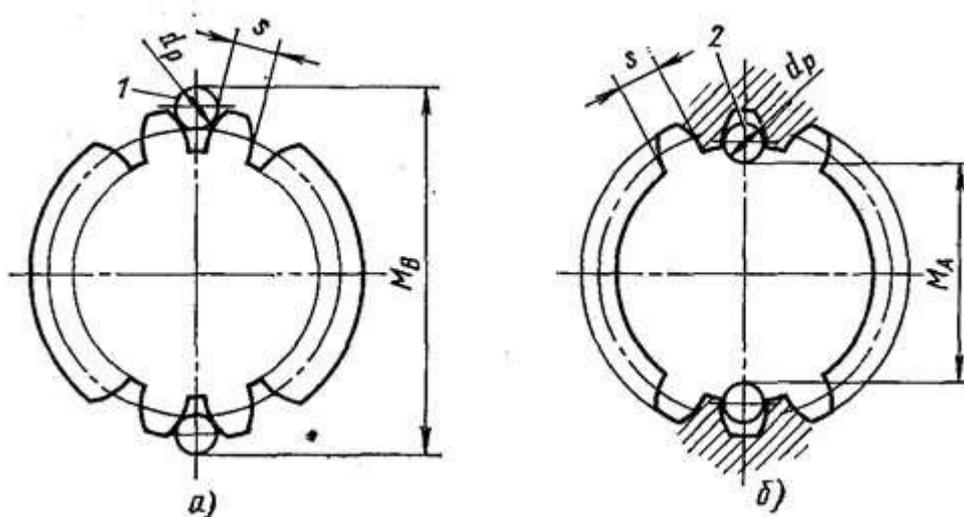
Схемы контроля толщины зуба и ширины впадины шлицевых деталей с эвольвентным профилем зуба
